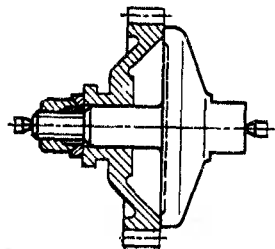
Схема установки заготовок насадных колес на швинговальном станке с горизонтальной осью заготовки
